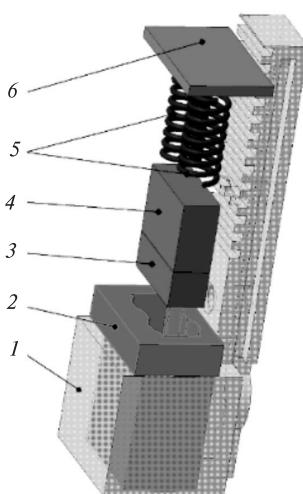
Конструкция дополнительного щеткодержателя под установку смазывающей щетки на турбогенератор мощностью 320 МВт: 1 – штатный щеткодержатель; 2 – дополнительный щеткодержатель; 3 – контактная часть смазывающей щетки; 4 – несущая часть смазывающей щетки; 5 – спиральные пружины; 6 – крышка
